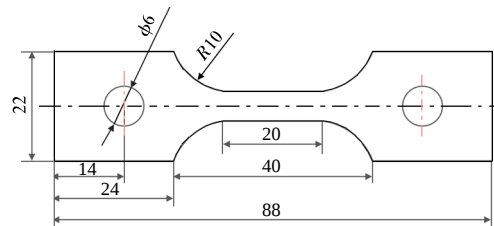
拉伸及持久力学性能试样形状及尺寸(mm)
